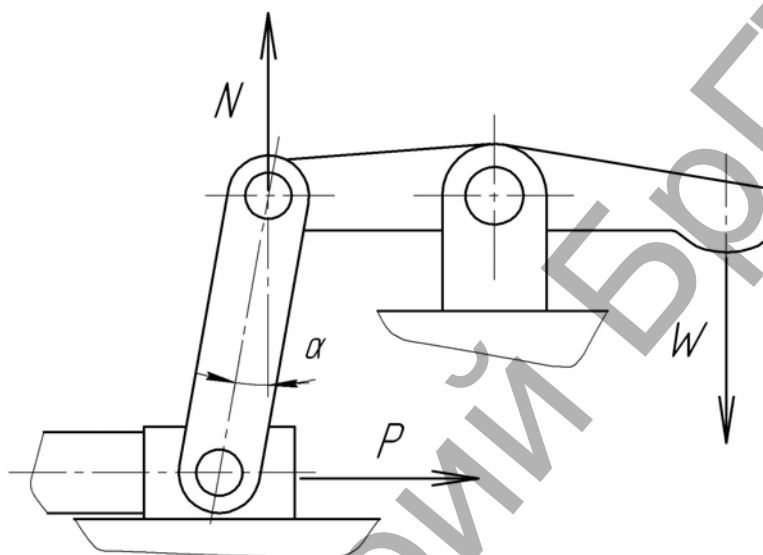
Однорычажный шарнирный зажимной механизм с ползуном
